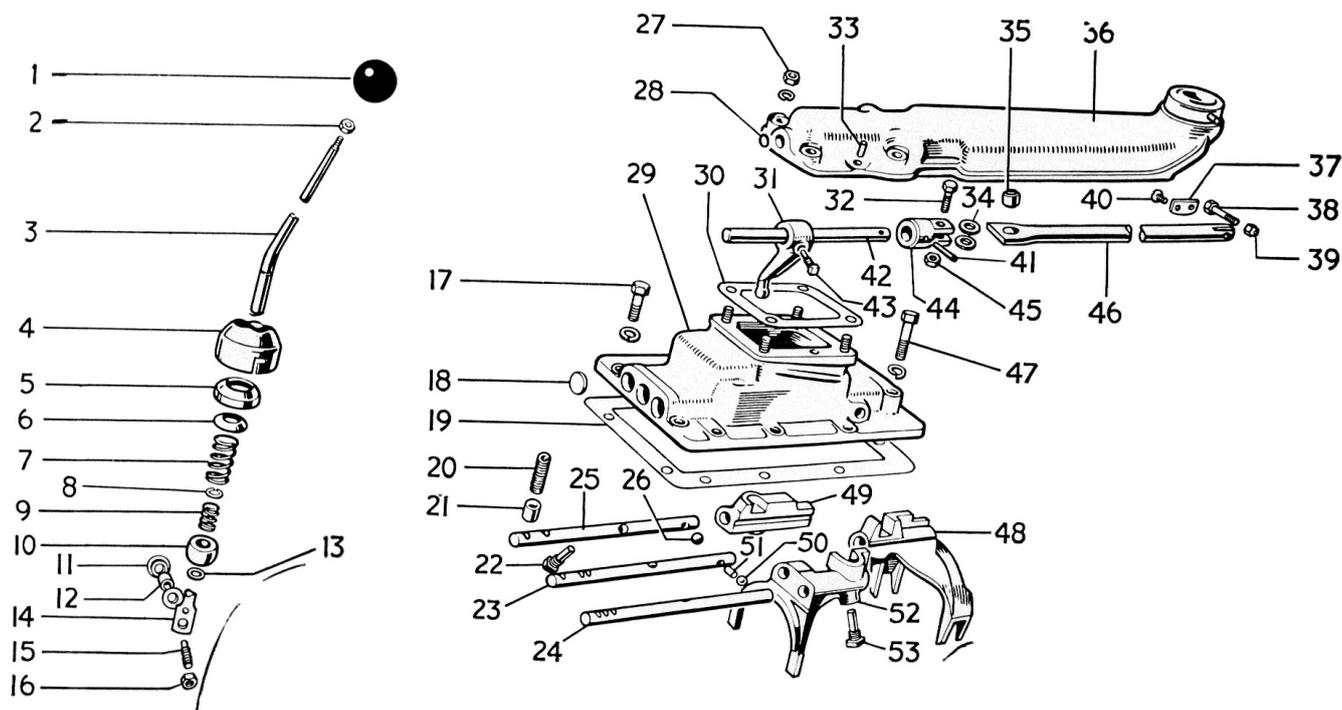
Vue éclatée de l'ensemble couvercle supérieur
